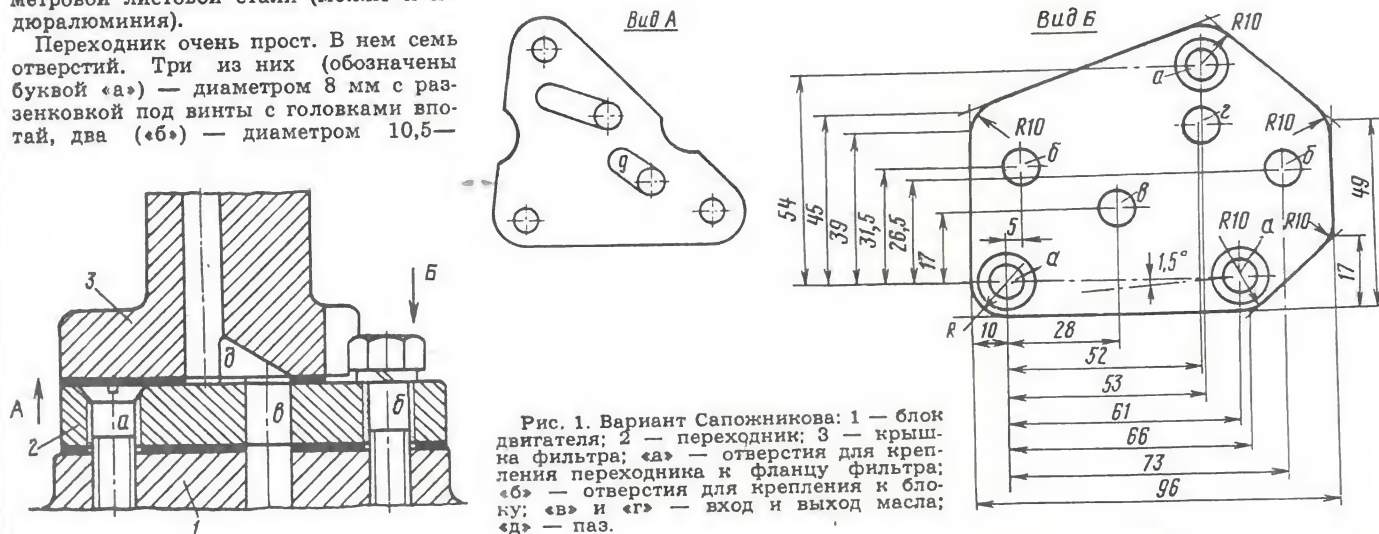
Вариант Сапожникова: 1 — блок двигателя; 2 — переходник; 3 — крышка фильтра; «а» — отверстия для крепления переходника к фланцу фильтра; «б» — отверстия для крепления к блоку; «в» и «г» — вход и выход масла; «д» — паз.
